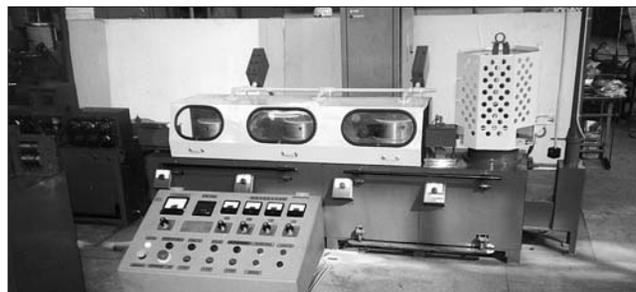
Четырехбарабанный волочильный стан конструкции ОАО «НИИМонтаж»
